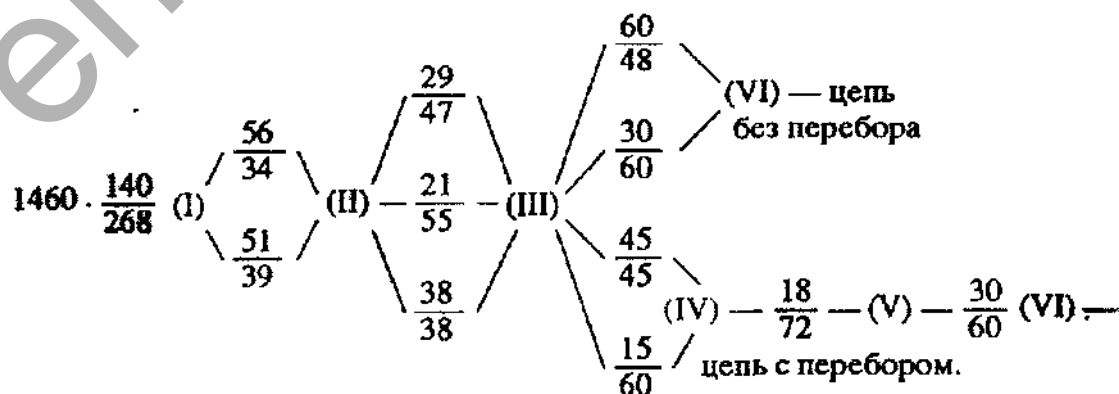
Структурная схема токарно-винторезного станка
